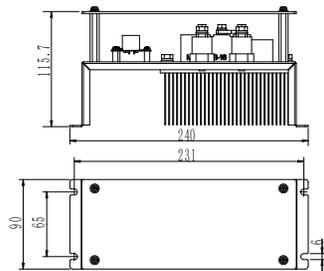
Dimensiones de instalación del módulo de (unidades: mm)
